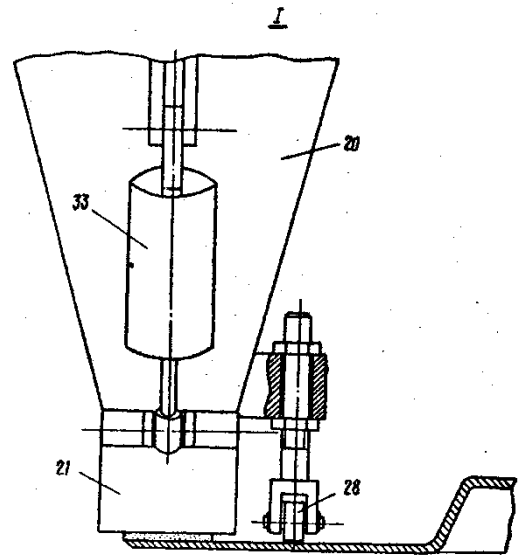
Механізм для регулювання товщини засипання шихти на поверхню диска до наплавлення (вузол I)
